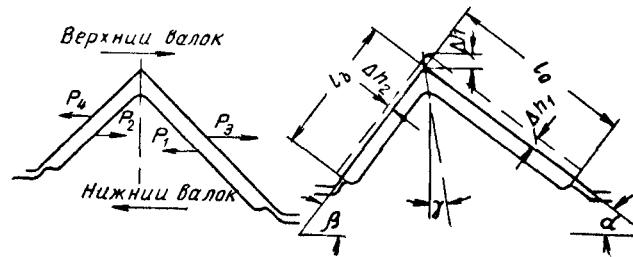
Калибровка чистового калибра для прокатки неравнобоких уголков
